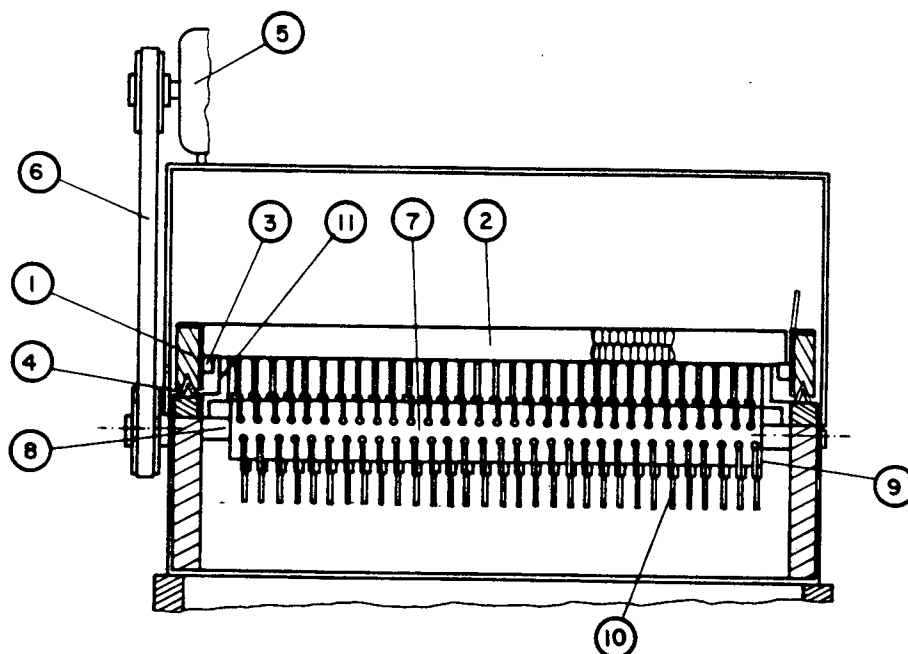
Vista frontal da desoperculadora tipo com um rotor [10].
